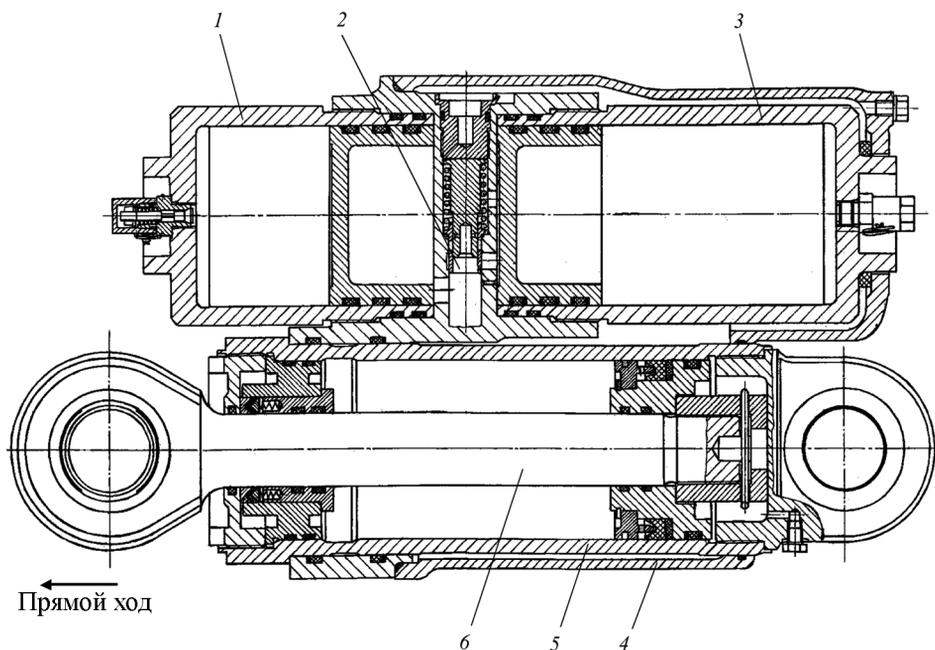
Конструкция ПГР с двумя ступенями давления:
